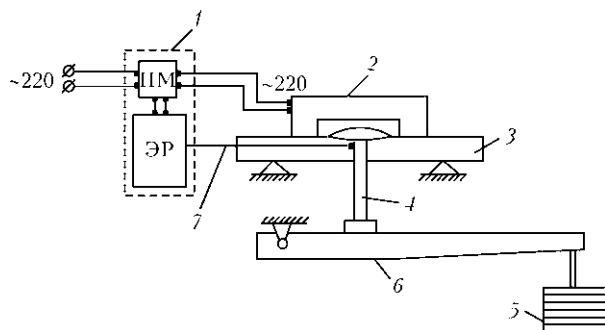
Принципиальная схема испытания «Implant» с нагревом сварного соединения: 1 — блок управления нагревом (ЭР — электронный регулятор температуры, ПМ — пускатель магнитный); 2 — нагреватель; 3 — пластина; 4 — образец (Implant); 5 — блок грузов; 6 — рычаг; 7 — термопара
